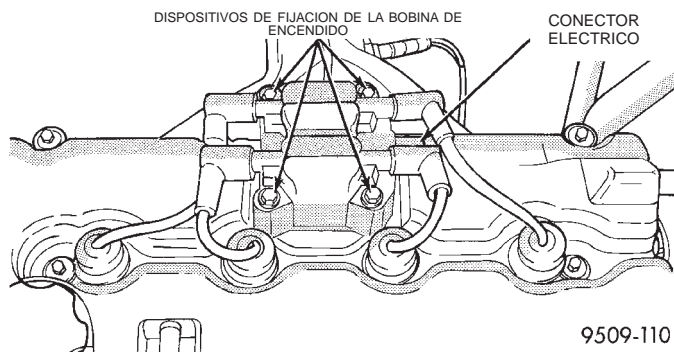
Conjunto de bobina de encendido electrónico—motor de 2.4L
